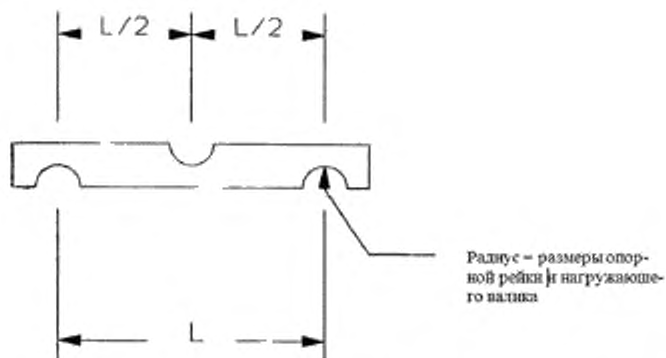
Приспособление, используемое для установки нагружающего валика, размещения опоры и выравнивания
